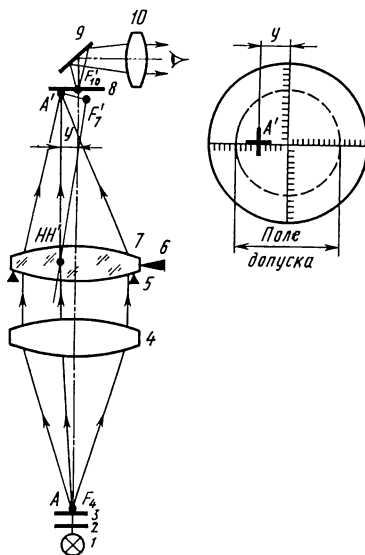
Схема коллиматорного прибора для измерения децентрировки и вид поля изображения
